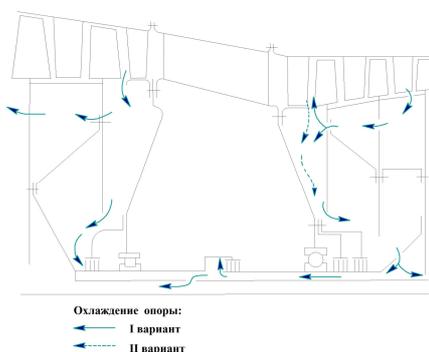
Два варианта наддува уплотнения опоры компрессора
